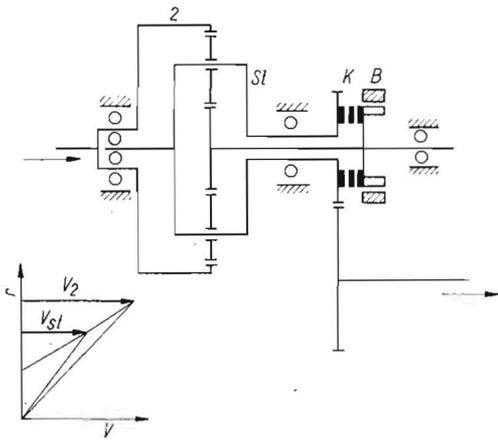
Unter Last schaltbares Planetengetriebe mit Drehzahlplan
